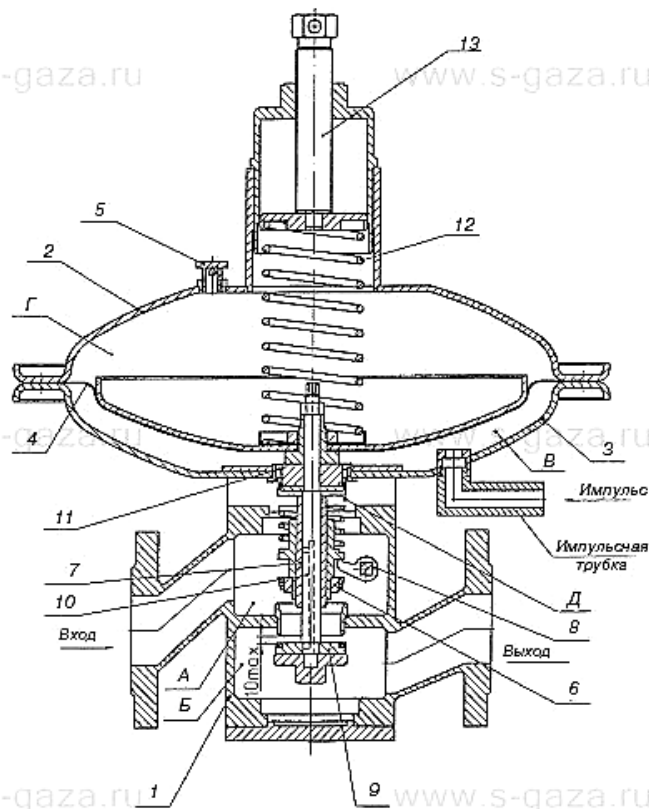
Устройство регулятора РДГПК-50: 1 — корпус регулятора; 2, 3 — крышки; 4 — мембрана; 5 — сапун; 6 — предохранительный клапан; 7 — направляющая; 8 — рычаг; 9 — клапан регулятора; 10 — шток; 11 — манжета; 12 — пружина; 13 — винт
